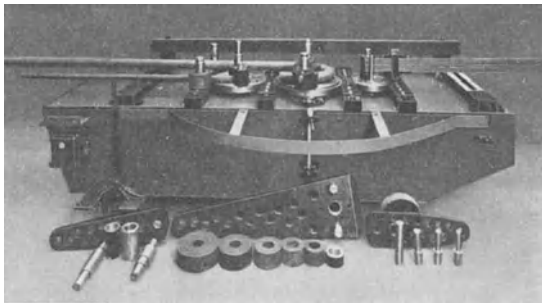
Biegemaschine „Standard-Record-Dubell“ für 60 mm Rundeisen.
